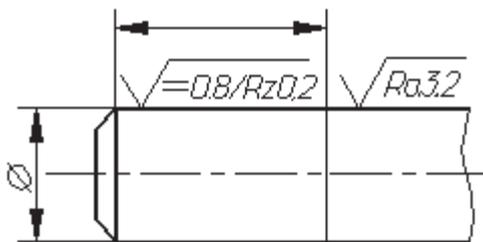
Пример обозначения различной шероховатости на одной поверхности
